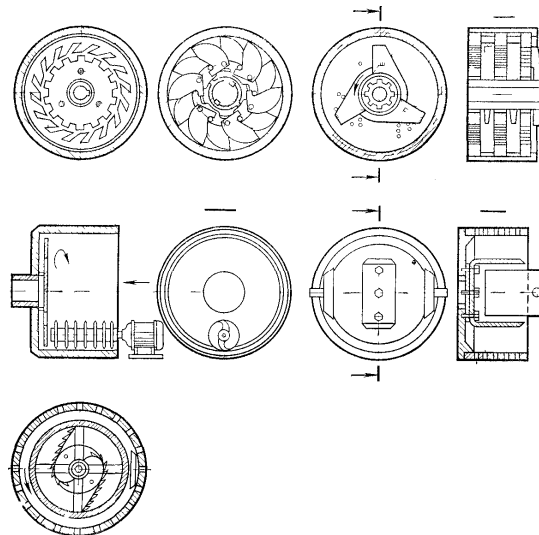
Схеми подрібнювачів: а) роторного типу; б) та в) багатоножового; г) багатодискового; д) барабанного; е) комбінованого
